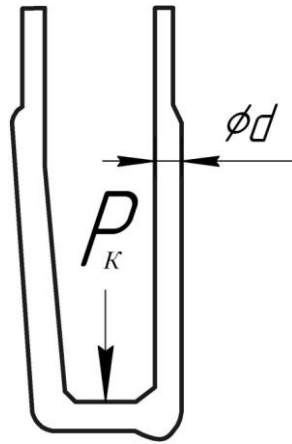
Розрахункова схема маятникової підвіски башмака
